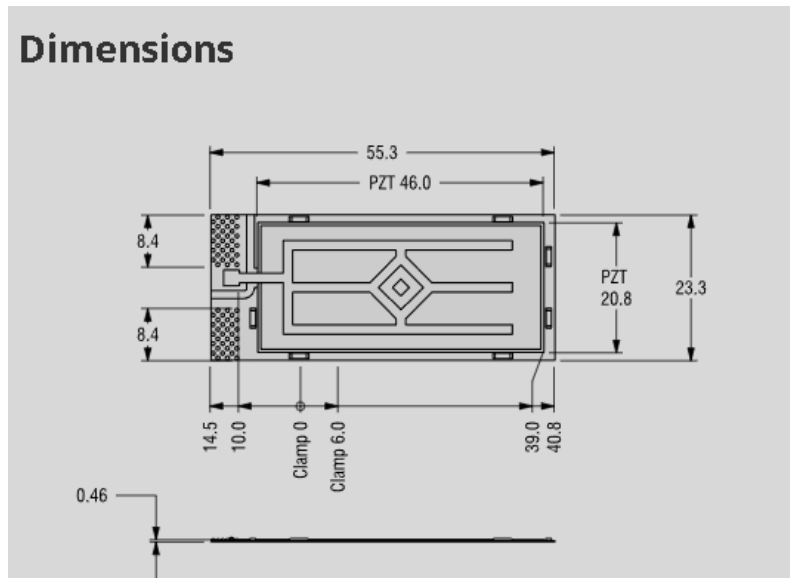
Dimensiones en mm del transductor S118-J1SS-1808YB [JPG] [28].
